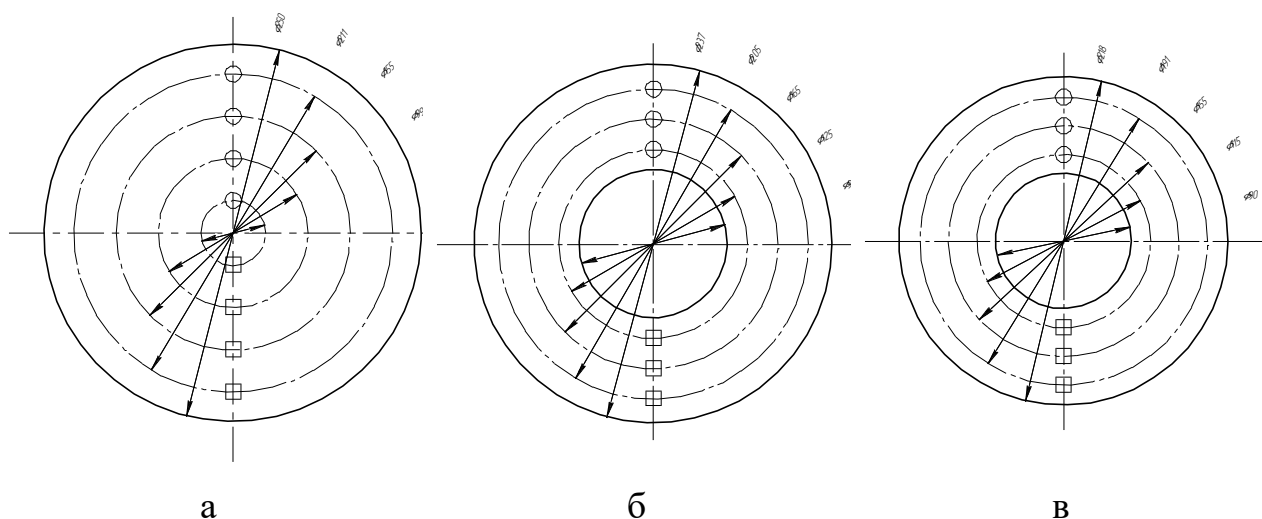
Схема вырезки образцов для механических испытаний из исходной заготовки (а), прошитої заготовки (б), черновой оси (в)
